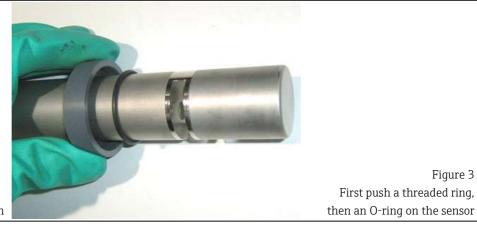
Erst einen Schraubring, dann O-Ring, auf den Sensor schieben
